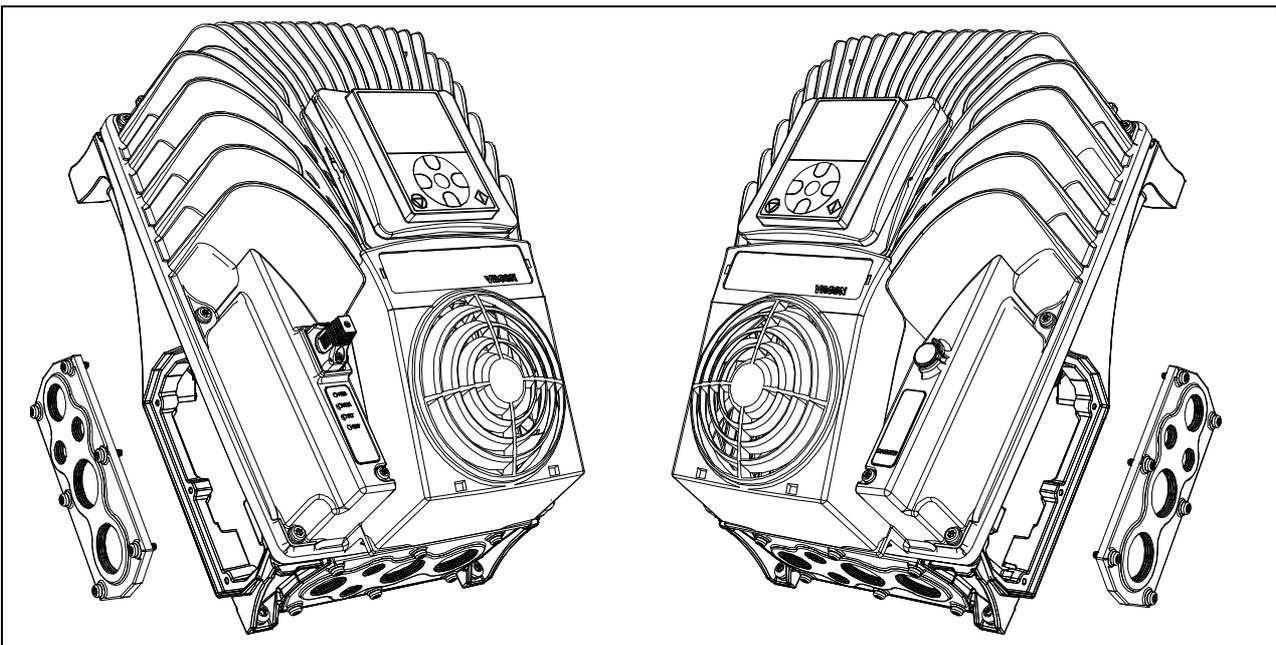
Die Kabeleinführungsplatte entfernen: Beispiel für Baugröße MM5.
